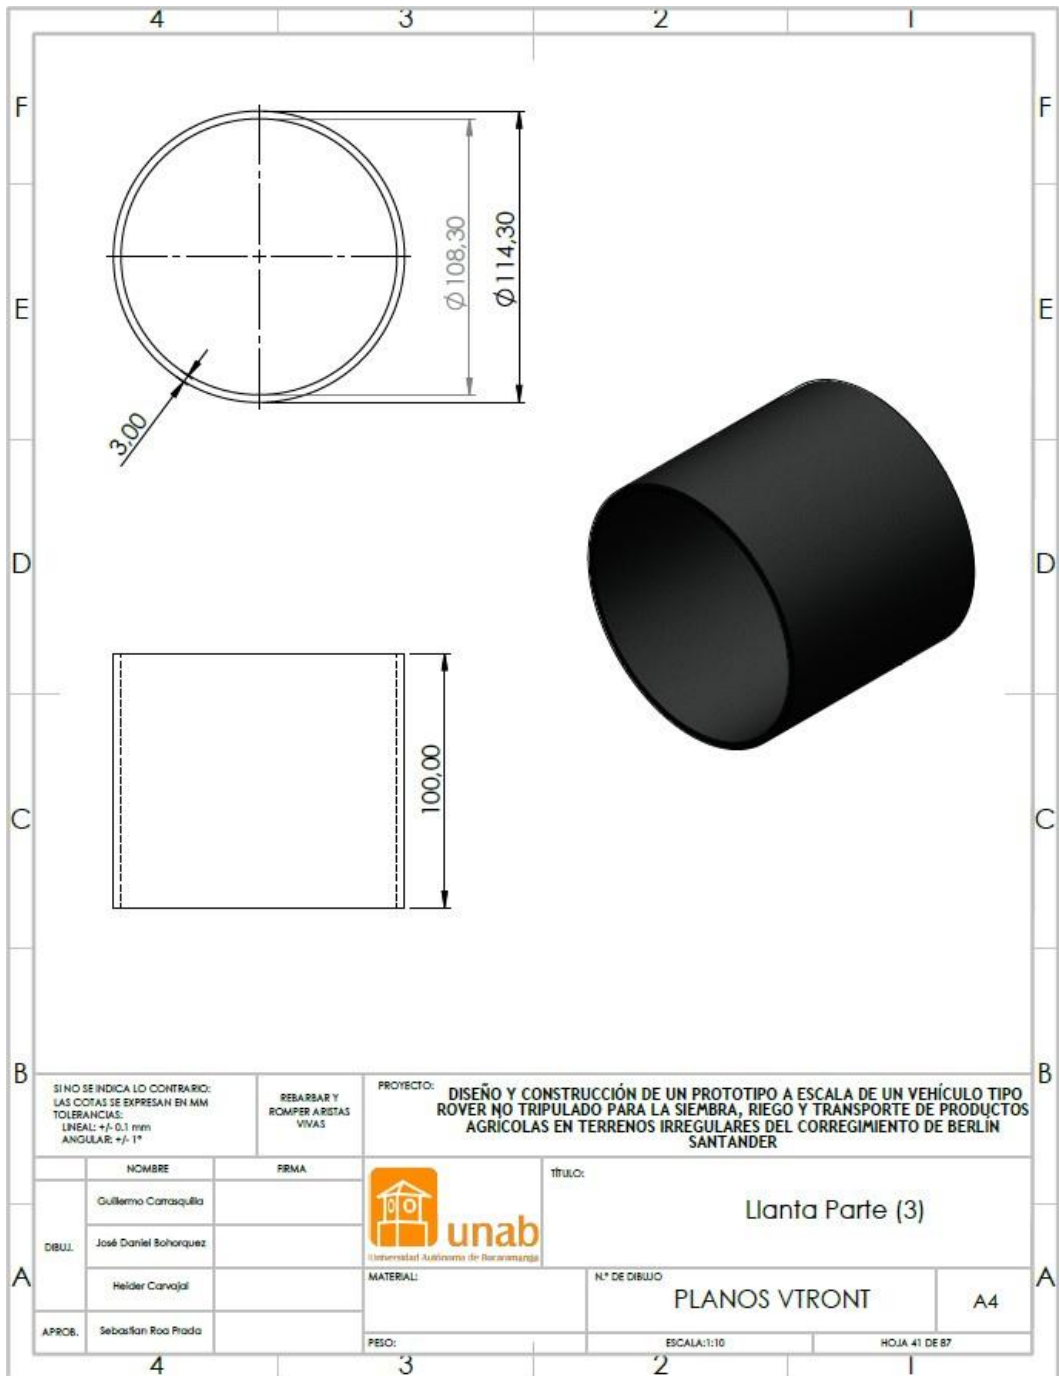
Plano de corte de tubería para la llanta parte 3.
